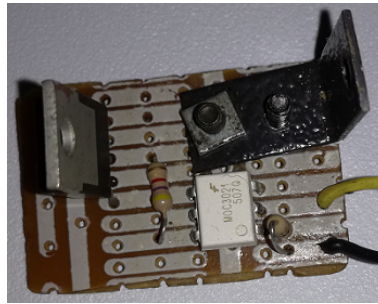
Circuito de sincronización implementado sobre PCB universal.
